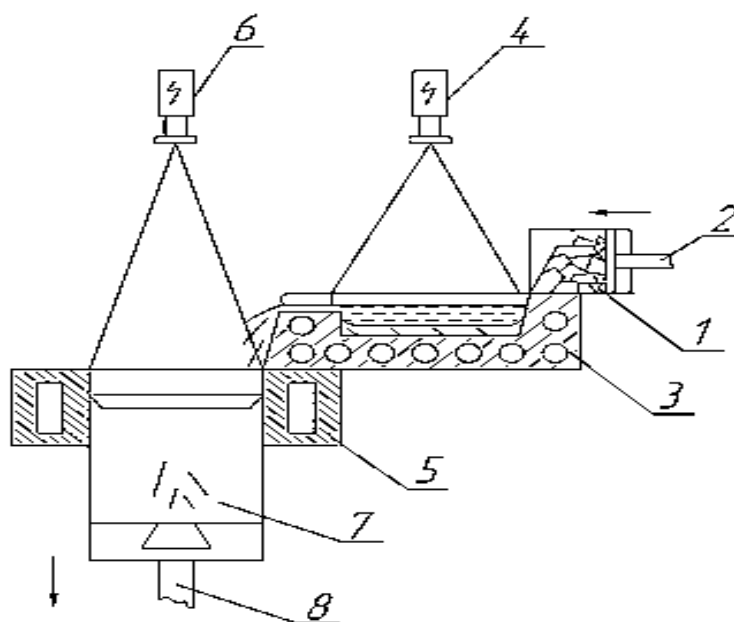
Схема ЕПП з ПЄ: 1 – шихта; 2 – механізм подачі шихти; 3 – ПЄ; 4,6 – ЕПГ; 5 – кристалізатор; 7 – зливочок; 8 – механізм витягування зливку
